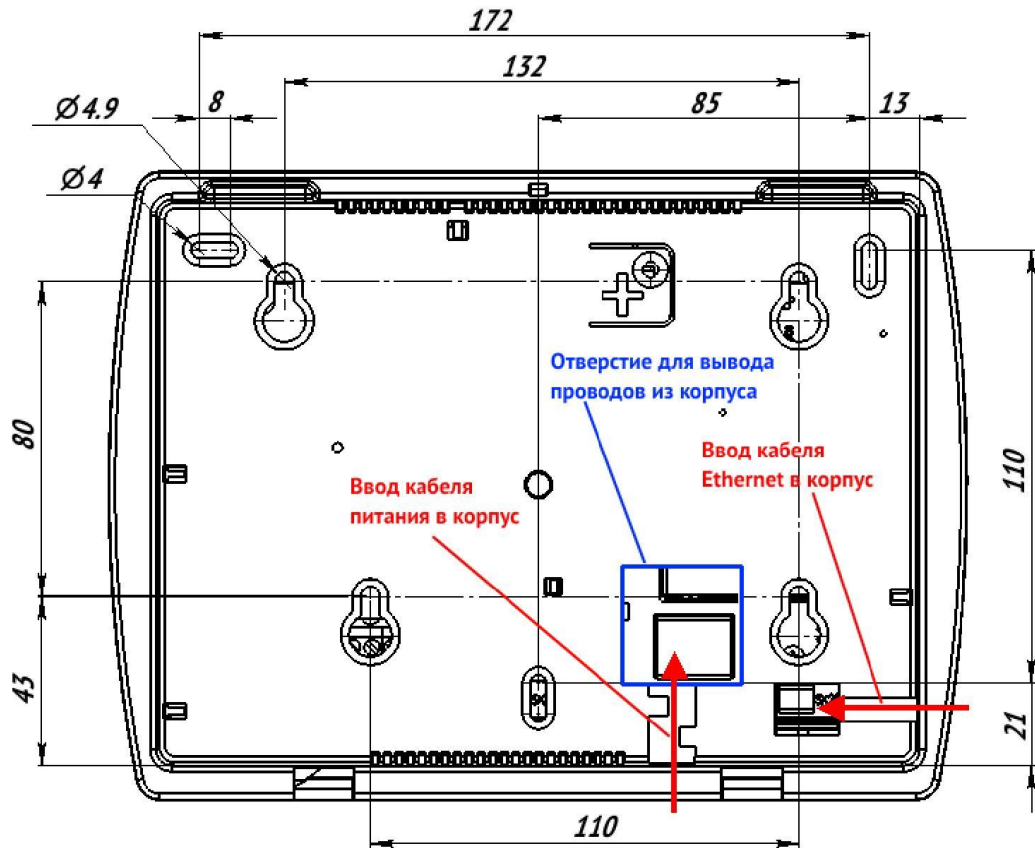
Установочные размеры корпуса ППКОП "Лунь-19" (вид со стороны установки)
